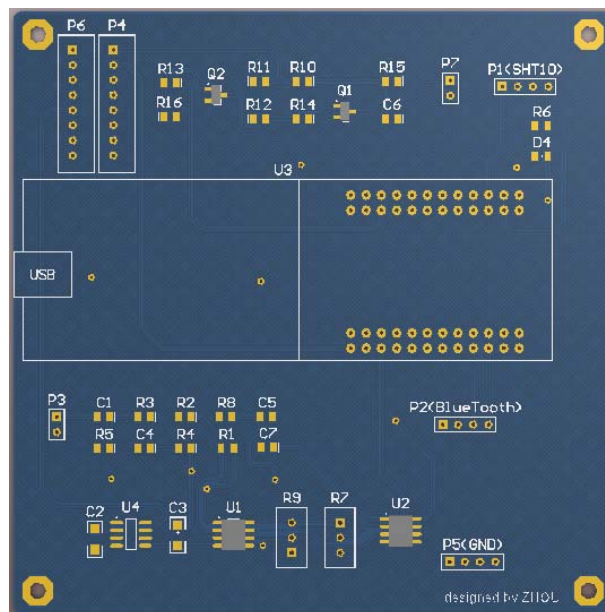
使用 Altium Designer 开发的 PCB 图（3D 视图）
